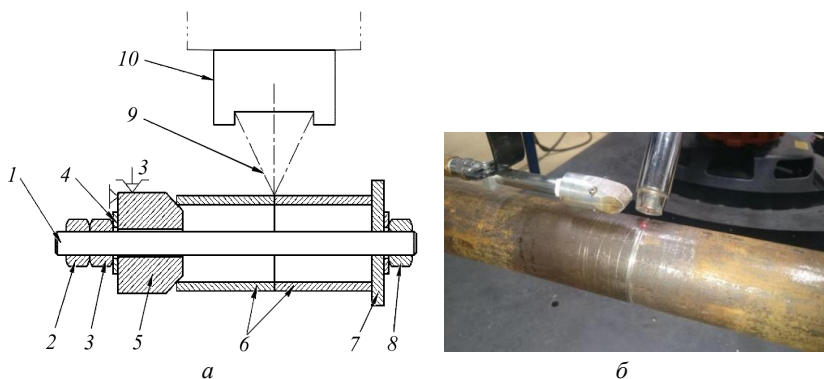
Приспособление для лазерной сварки труб: *а* – общий вид; *б* – сборочная схема; 1 – шпилька; 2 – гайка; 3 – контргайка; 4 – шайба; 5 – конусный упор; 6 – стыкуемые трубы; 7 – зажимная шайба; 8 – зажимная гайка; 9 – схема фокусировки лазера; 10 – лазерная сварочная голова Kugler
